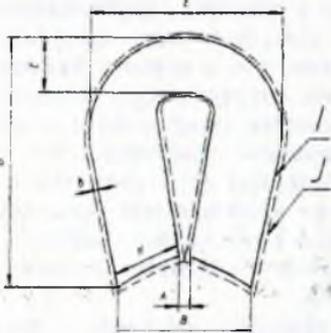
Контрольные размеры детали типа "блочный ремешок"
